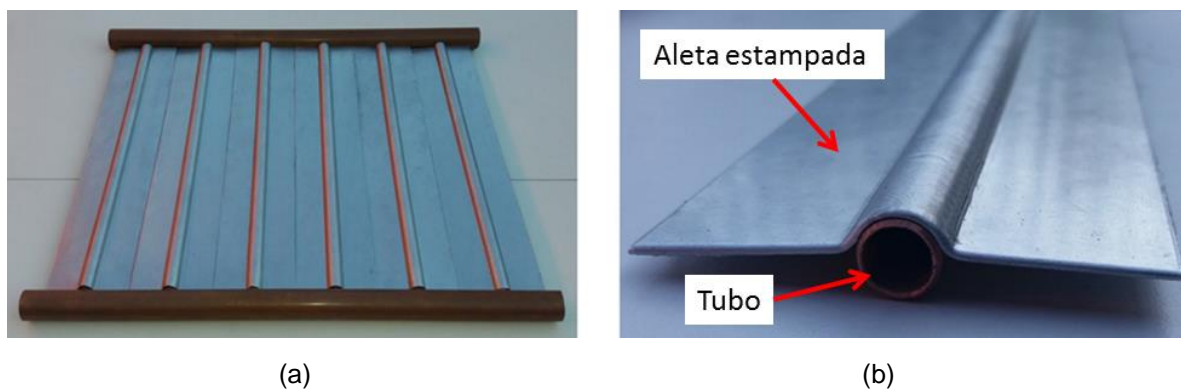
Protótipo de Aleta de Coletor Solar fabricada por Estampagem Incremental: (a) Conjunto de aletas montadas na serpentina de tubos de cobre e (b) Detalhe de montagem da aleta estampada sobre tubo de cobre [9]
